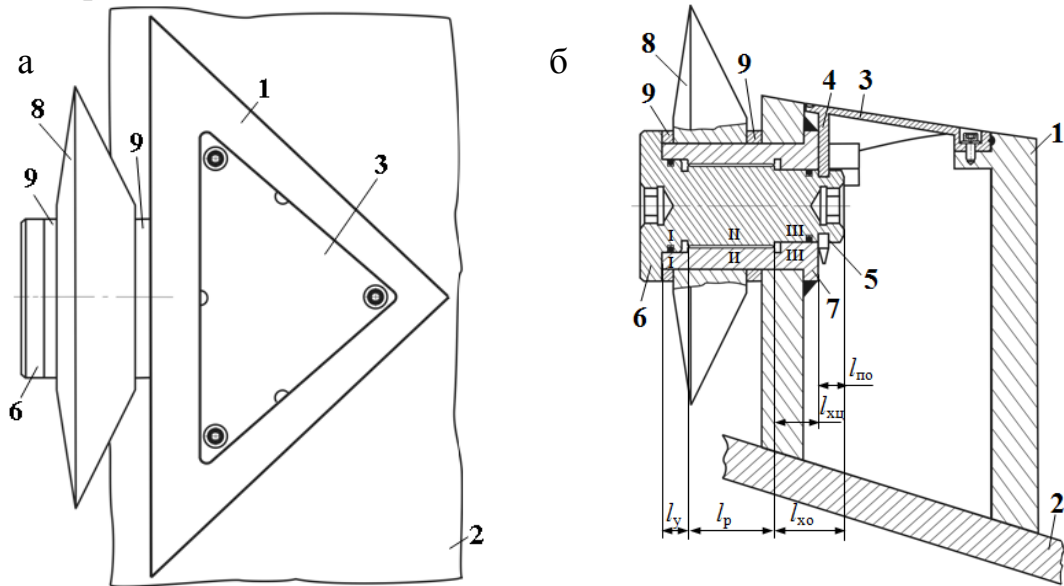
Устройство трехгранной призмы с узлом крепления дискового инструмента: а – вид сверху; б – радиальное сечение
